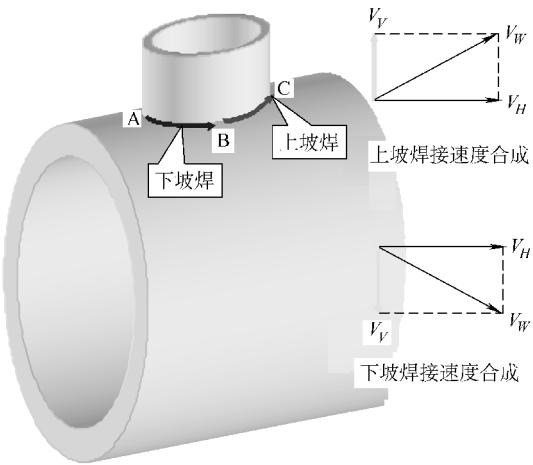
马鞍形焊缝焊接的速度合成
